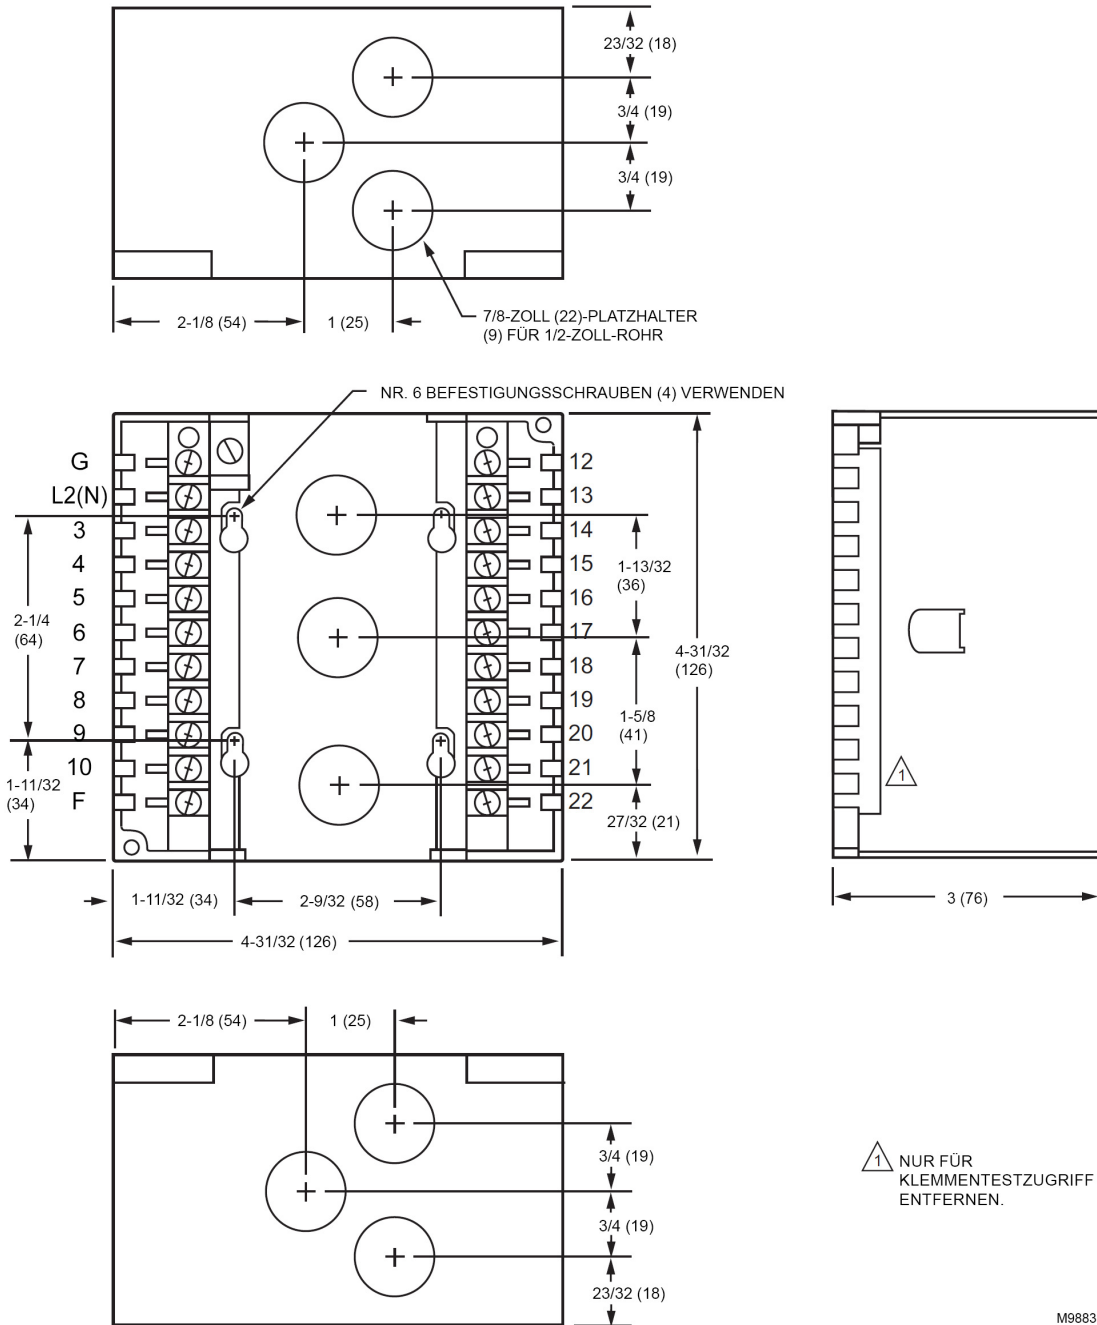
Draufsicht und Frontansicht des Q7800B1011-Verdrahtungssockels (4-seitig) mit Abmessungen in Zoll (mm).
